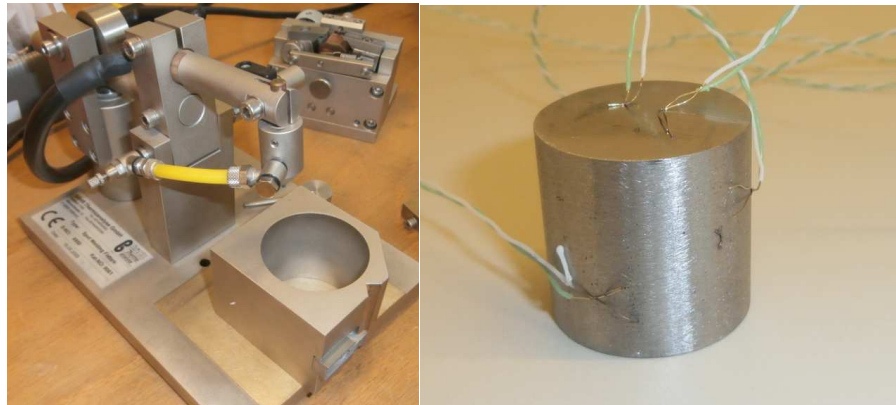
Soldador de puntos (izquierda). Probeta con los termopares soldados (derecha).
